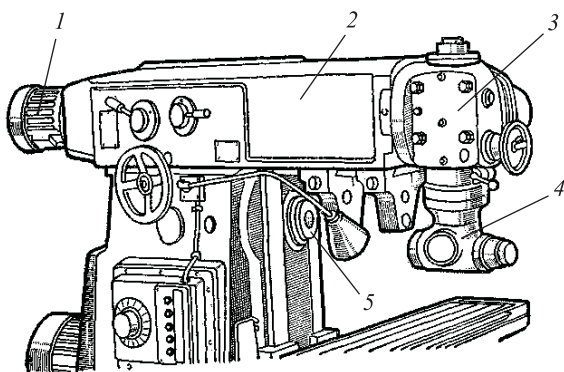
Конструктивные особенности широкоуниверсального консольно-фрезерного станка модели 6P82Ш
